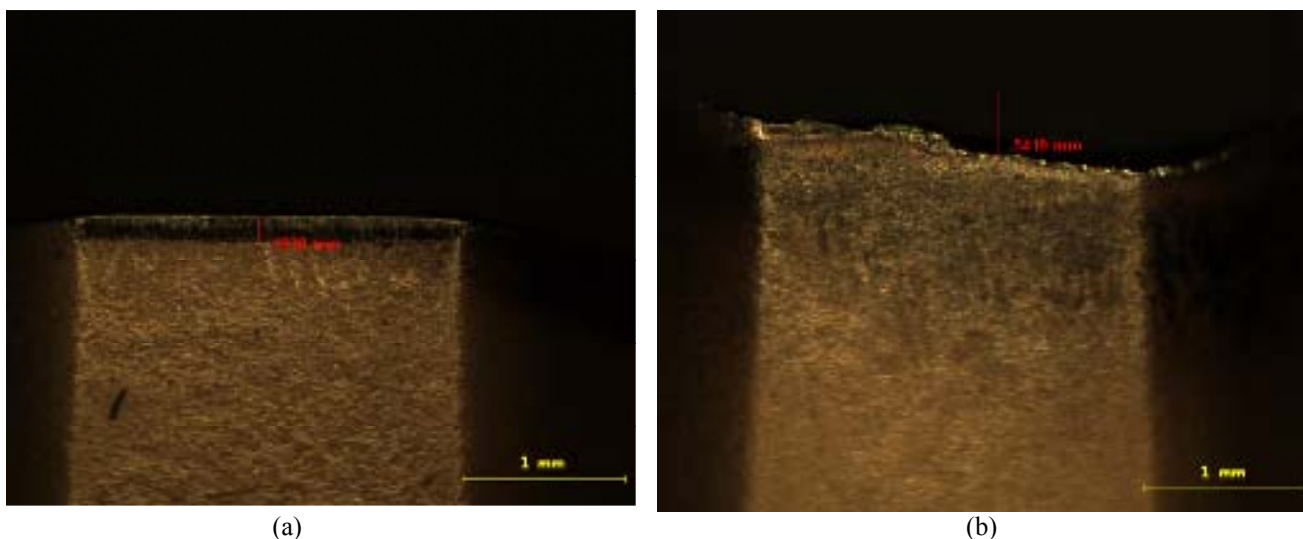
Imagem do desgaste da ferramenta de metal duro após usinagem com fluido de corte pela técnica MQF com  $V_c=200$  m/min e  $f_z=0,14$  mm/volta para a entrada a  $45^\circ$ ; a) 1º passe; b) 13º passe (lascamento)
